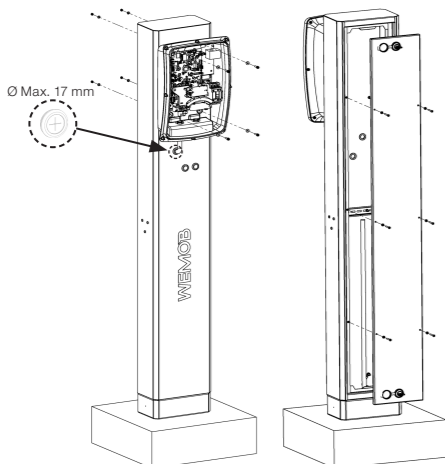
Ejemplo de fijación de la estación WALL G2 en el Tótem
